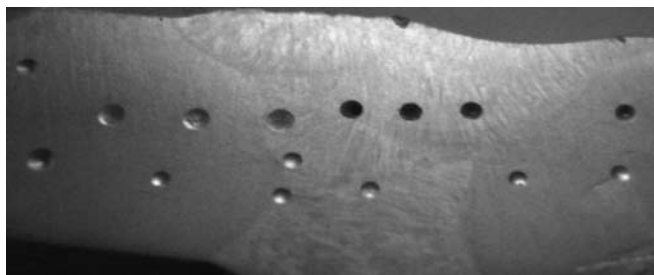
Aspecto macrográfico da junta soldada antes da usinagem do corpo de prova, com as indentações relativas às medidas de dureza.
